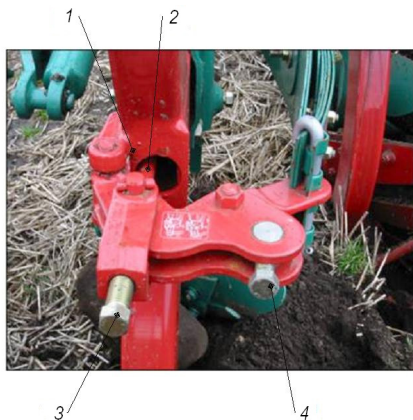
Регулировка предохранителя: 1 – труба; 2 – тяга; 3, 4 – болты
